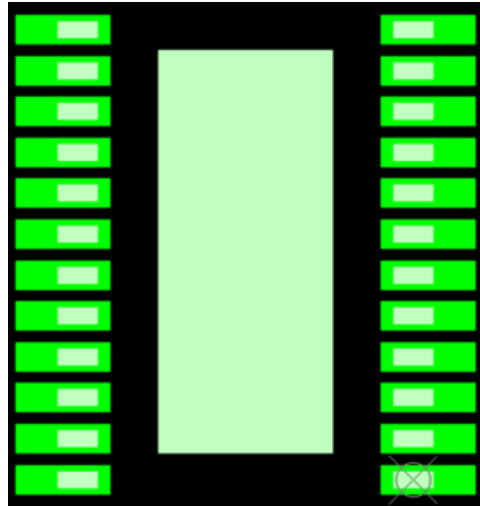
PWP0024T PCB 焊盘上的 SO-24，白色：其他 SO-24 引线，绿色：TI PWP0024T PCB 焊盘
